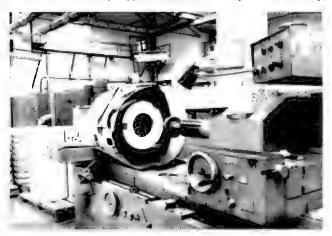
Общий вид токарно-лобового станка модели РТ-102 для обработки кругов диаметром до 500 мм
